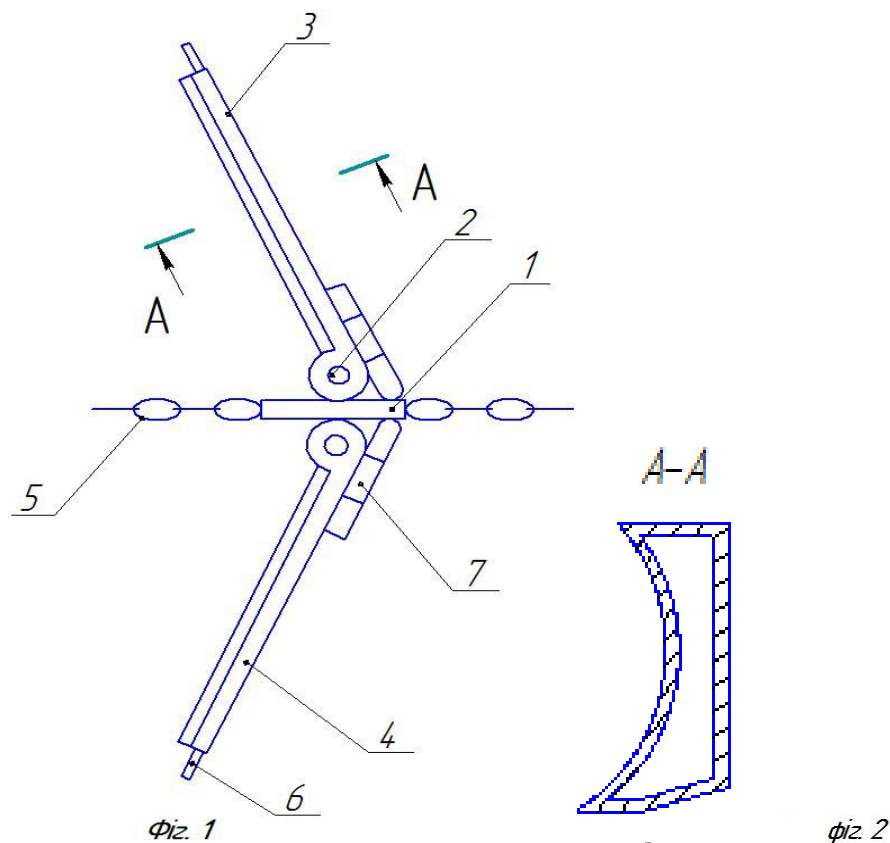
Розроблений скреперний пристрій для прибирання гною.
